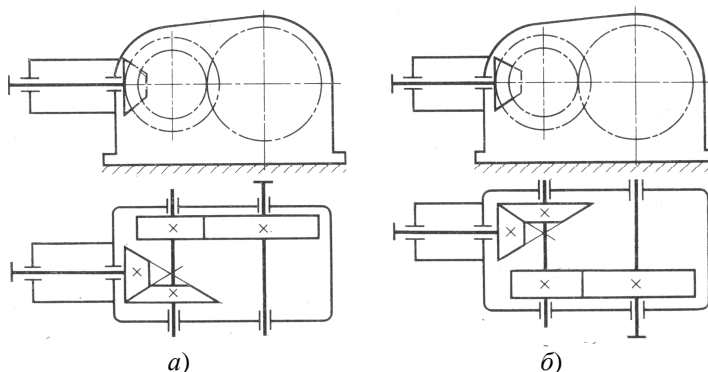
Двухступенчатые коническо-цилиндрические редукторы
